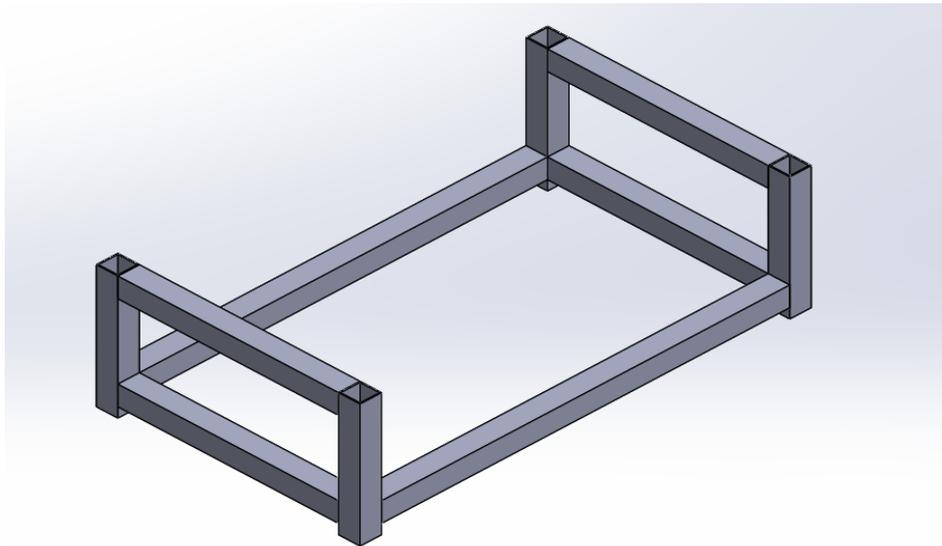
Structure de support en acier (tube carré) de la machine CNC 5 axes
